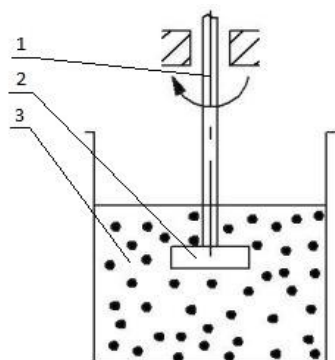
Схема обработки детали методом шпиндельной галтовки [2]
